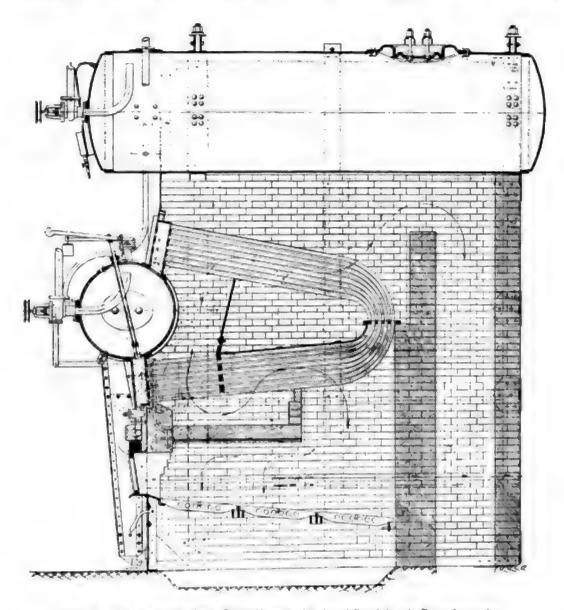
Längsschnitt eines Grille-Kessels für Land-Betrieb mit Dampfsammler
